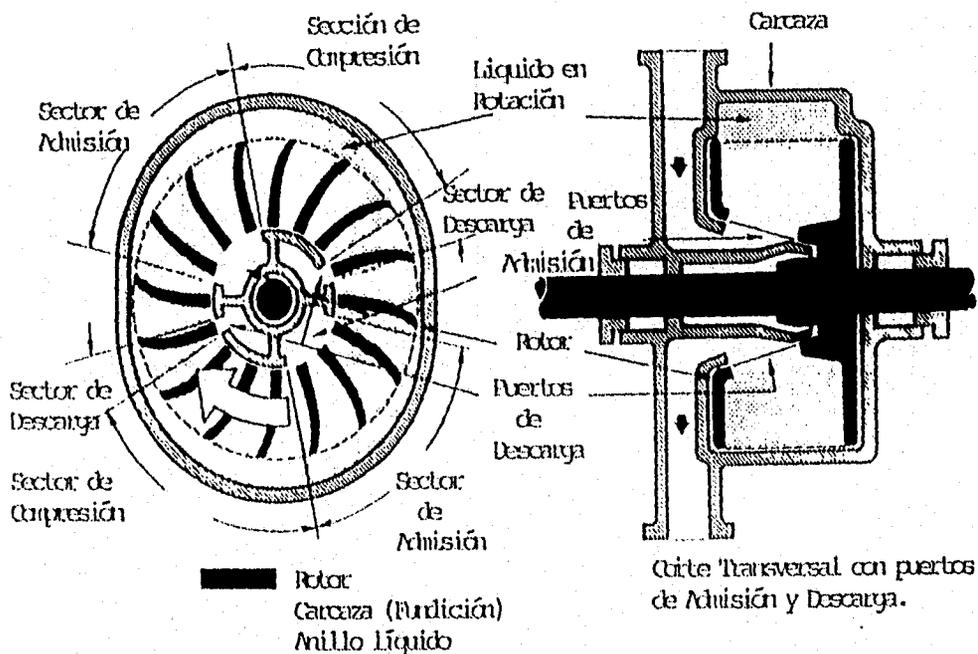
COMPRESOR DE ANILLO LIQUIDO
